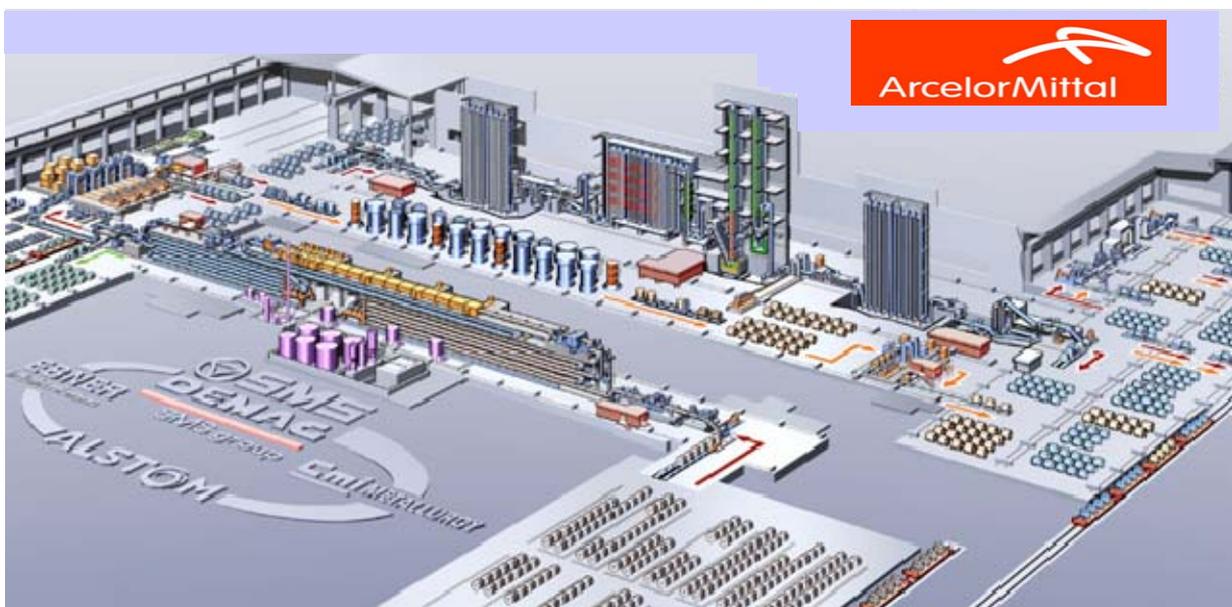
Esquemático da Planta da ArcelorMittal Vega
